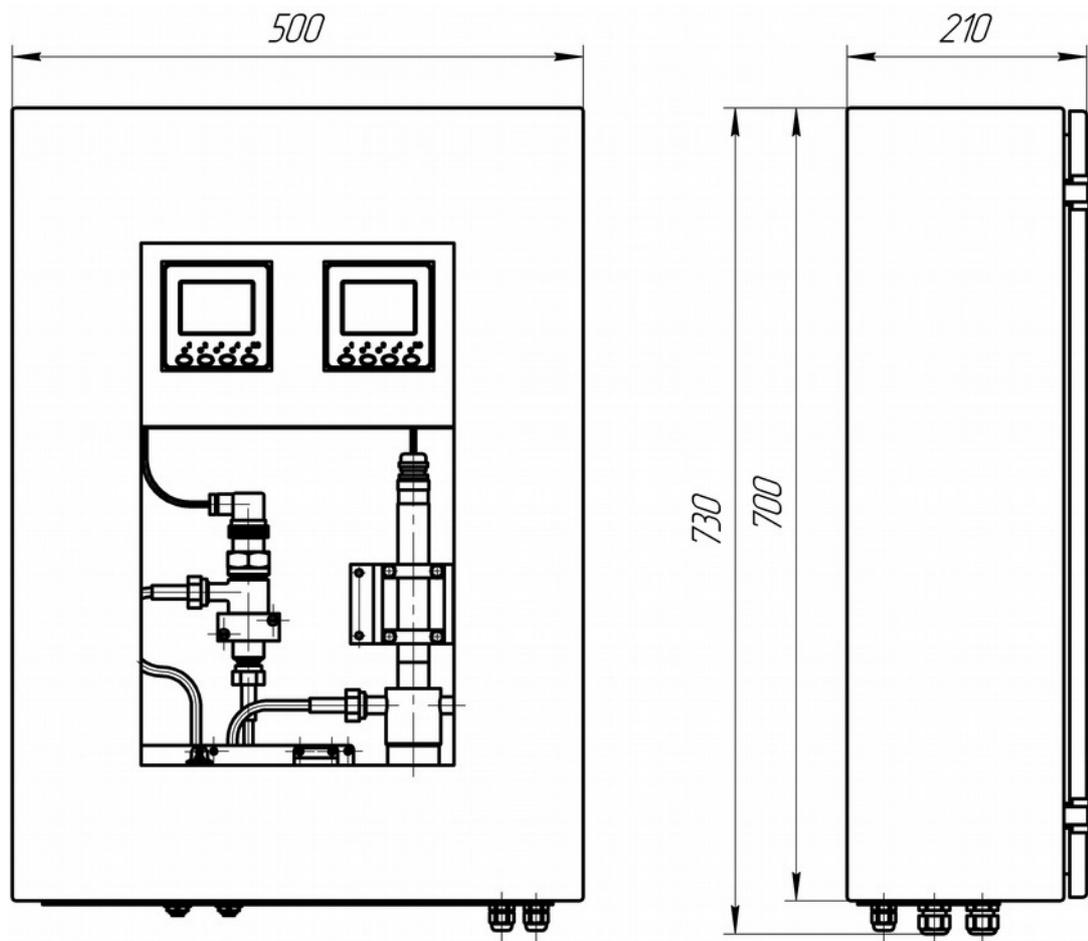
Габаритные размеры ШГП-АЖМ.01
